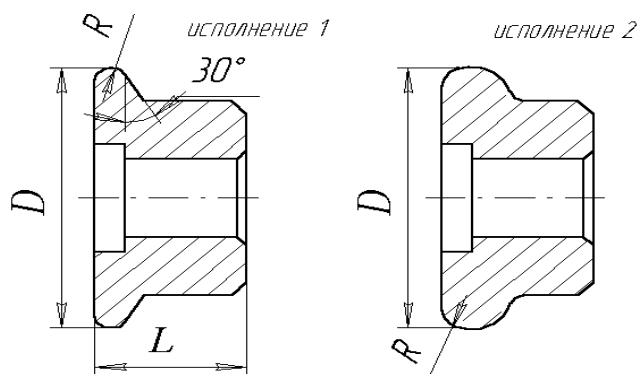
Ролики для упрочняющей обкатки поверхностей (по ГОСТ16344)
